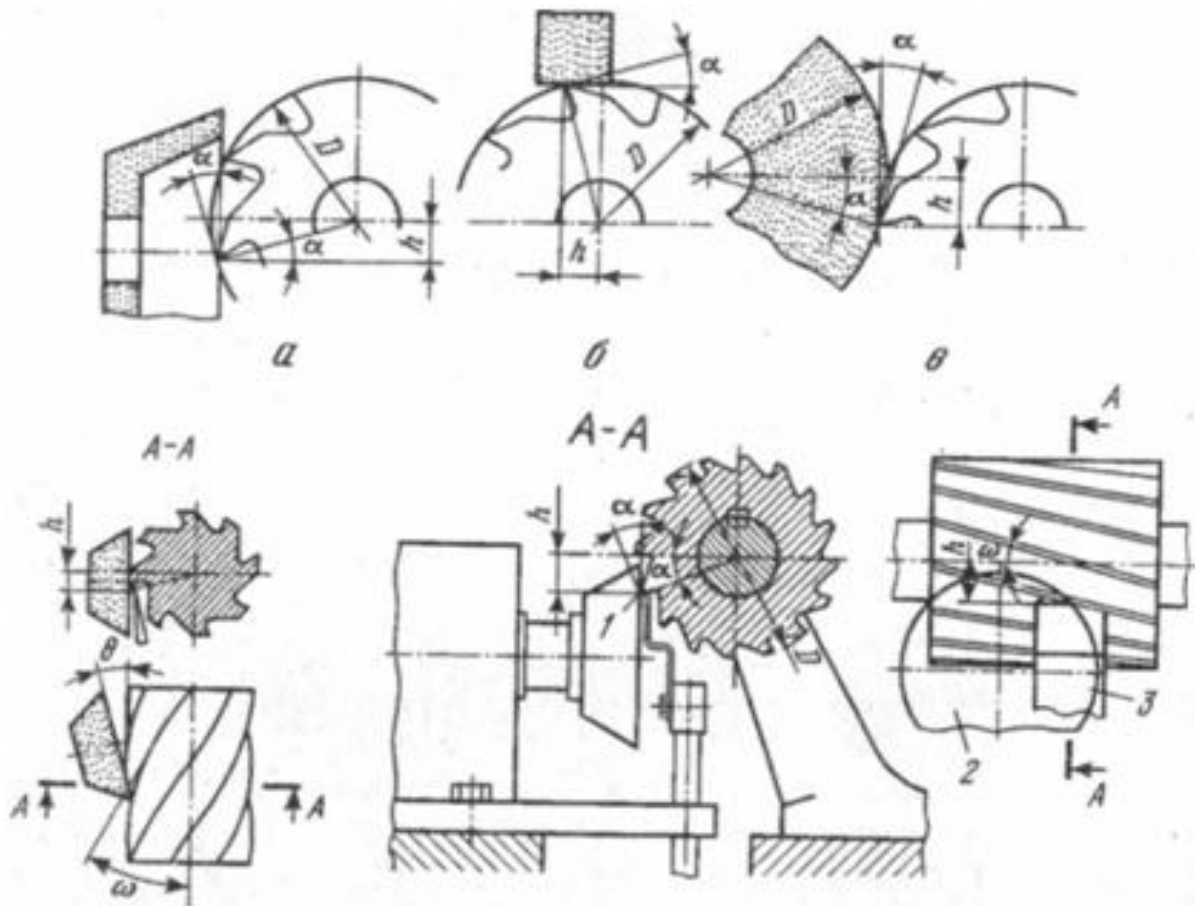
Схемы заточки задних поверхностей зубьев фрез.
